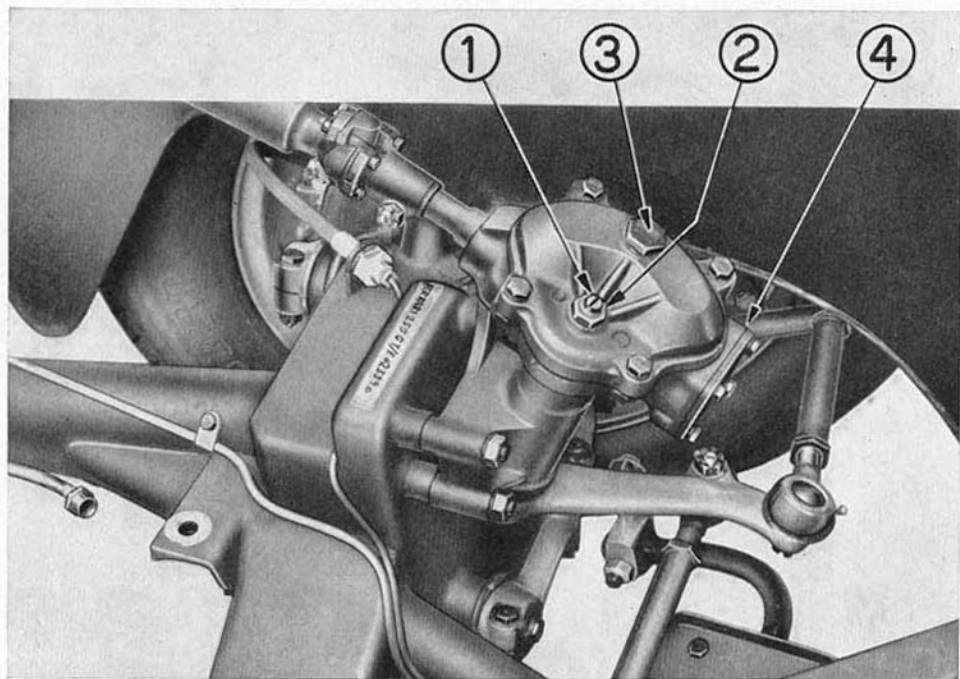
Boîtier de direction : 1) Vis de réglage; 2) Contre-écrou; 3) Bouchon de remplissage d'huile; 4) Epaisseur pour réglage des roulements.
